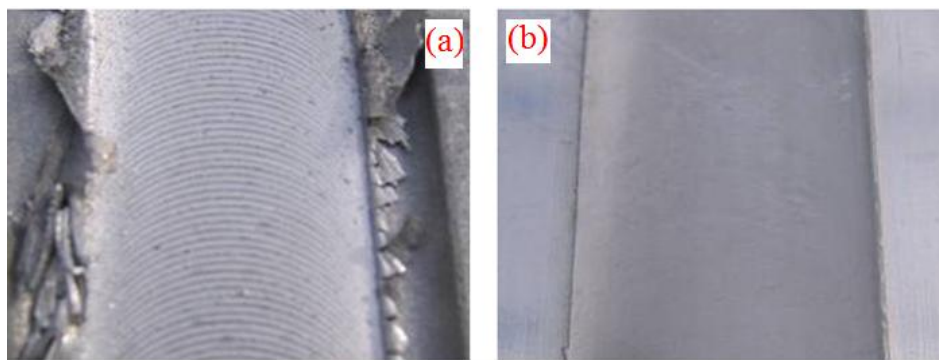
Surface d'un cordon de soudure FSW [34].
